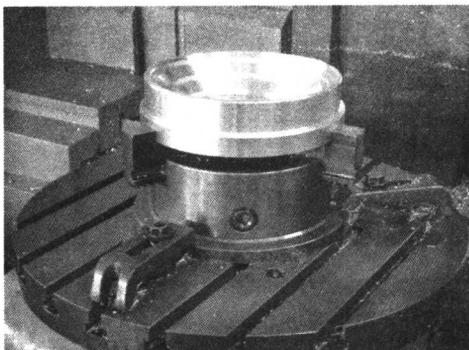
17 立式加工中心上使用三爪自定心卡盘装夹工件
